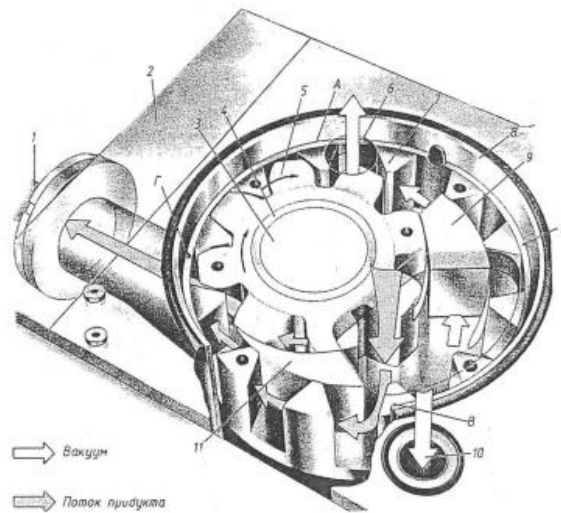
Шестеренний витиснювач з внутрішнім зачепленням фірми "Карл Шнель":
